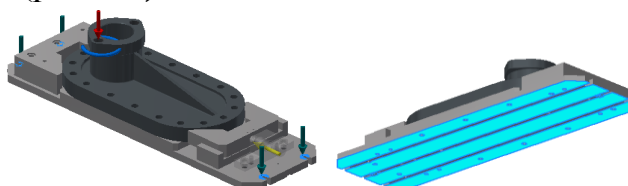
Выбранные поверхности и грани станочного приспособления при действии рабочих нагрузок
